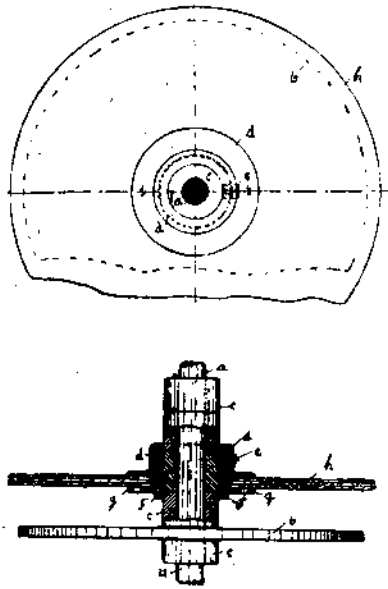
Ограждение фрезы, имеющей верхний добавочный подшипник.
